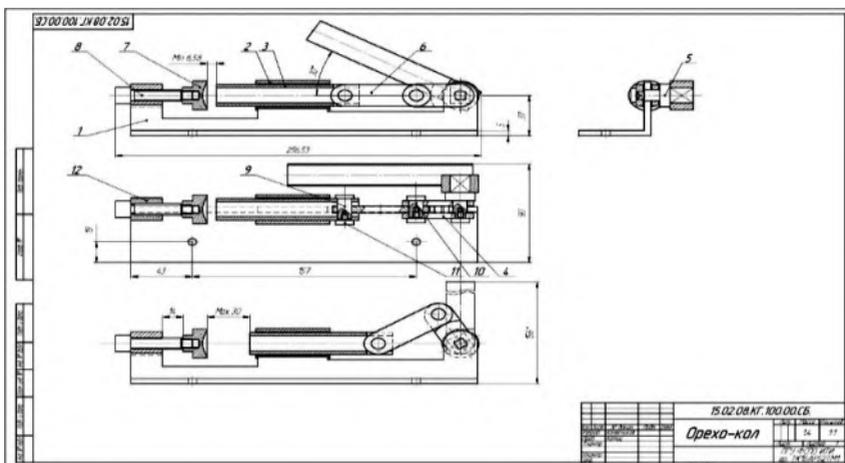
Фрагмент комплекта конструкторской документации – сборочный чертеж
